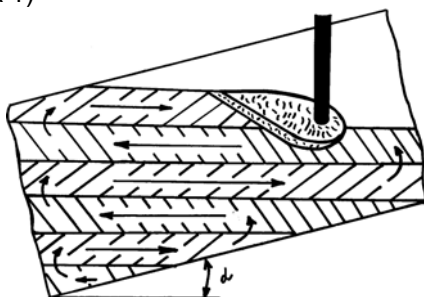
Схема шагодугового процесса сварки
